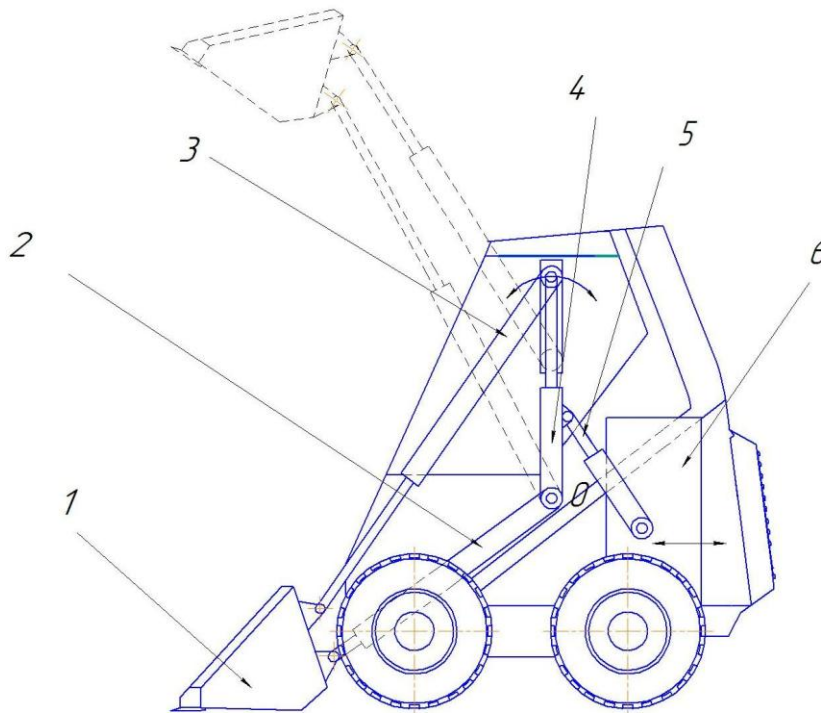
Техническое предложение конструкции УМП: 1-ковш; 2,3,4- гидроцилиндры подъема - опускания ковша; 5- дополнительный гидроцилиндр; 6- подвижный балластированный противовес
